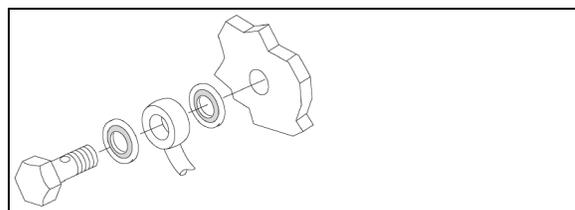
ACCESORIO DE COMPRESIÓN DE LÍNEA DE COMBUSTIBLE
